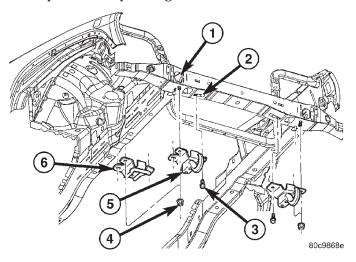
GANCHOS/ANILLA PARA REMOLQUE
